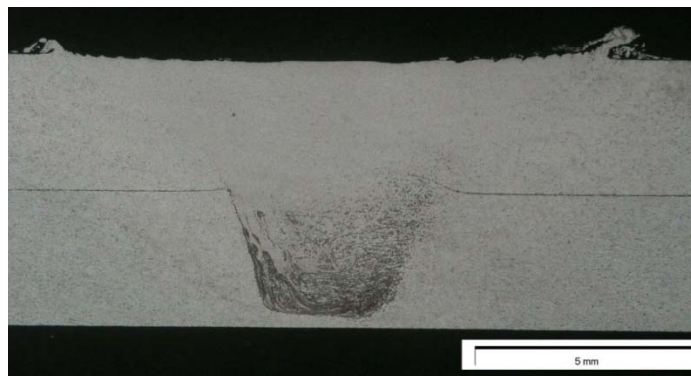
Macrographie d'une coupe transversale du soudage FSW par recouvrement (essai REC 2-1).
